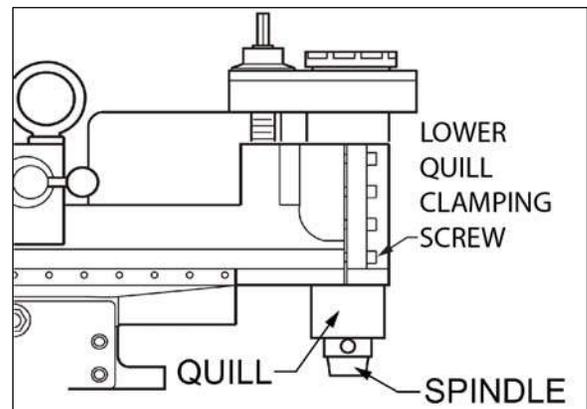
EMPLACEMENT DE LA VIS DE SERRAGE BAS DE L'ARBRE CREUX
